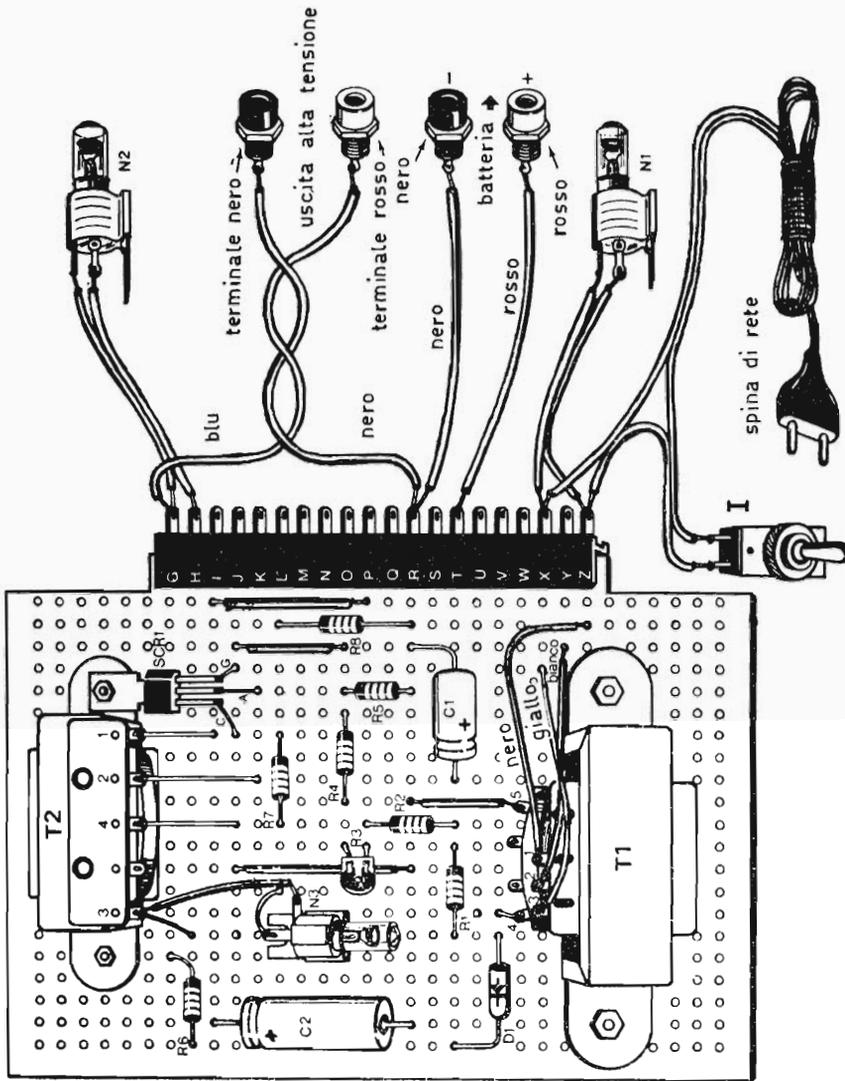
Vista del montaggio completo del pannello e della filatura dello stesso.
